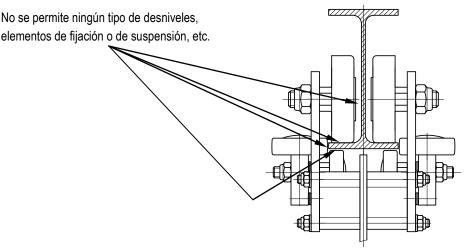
Ejecución sin desniveles de los soportes del perfil de rodadura soldados
